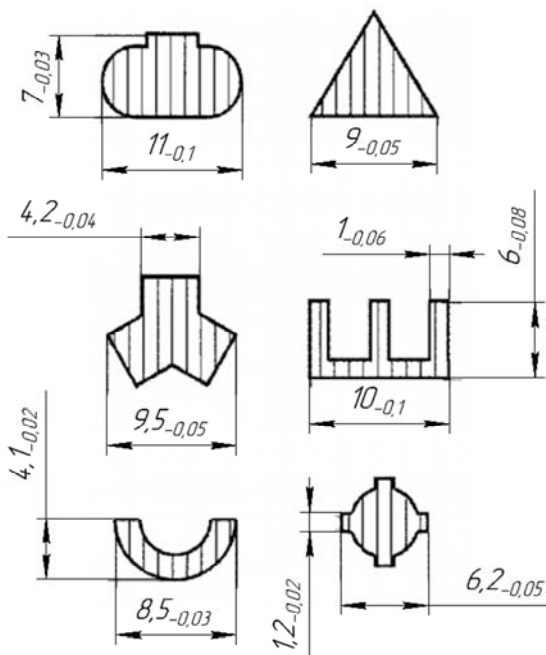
Примеры деталей из ферритов и керамики, полученные ультразвуковой размерной обработкой
